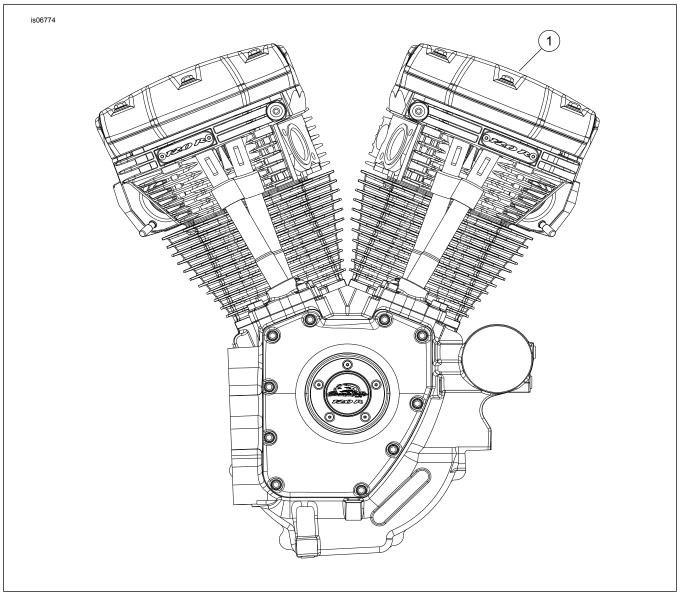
Conjunto del motor, motor ensamblado SE Pro 120R (Alfa) completo
